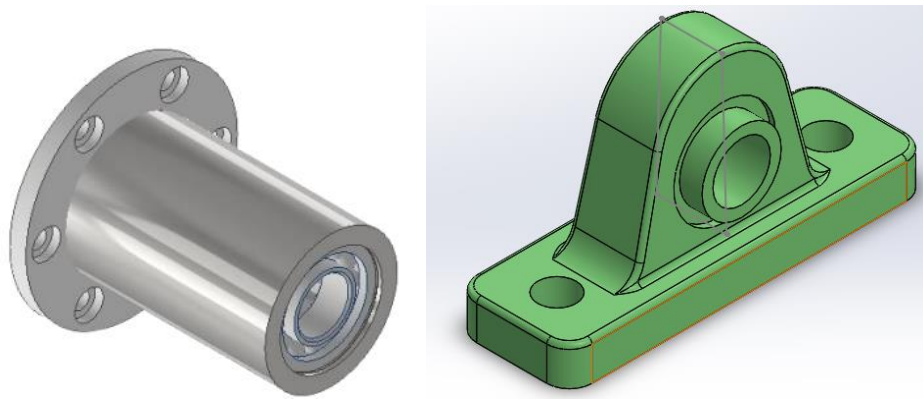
Vista 3D del soporte de rodamientos. Izq: diseño anterior [1], Der: diseño actual.
